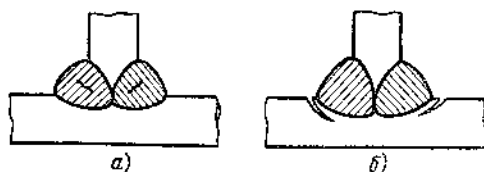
Трещины в сварных швах и соединениях:
